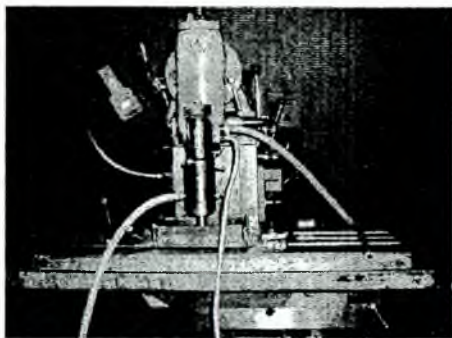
Внешний вид установки для ультразвуковой импульсной упрочняющей обработки поверхности плоских деталей на фрезерном станке.
